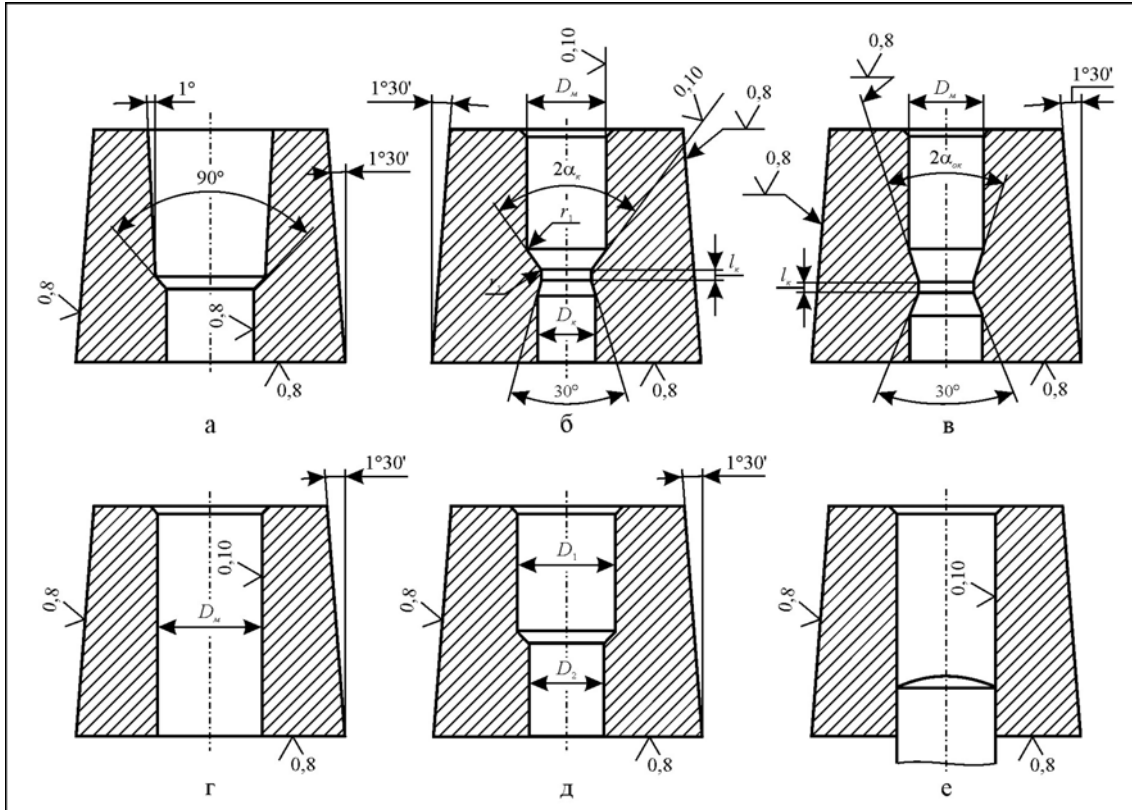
Конструкції матриць для ХОШ: а – для калібрування; б – для прямого видавлювання; в – для редакування; г, д, е – для зворотного видавлювання
